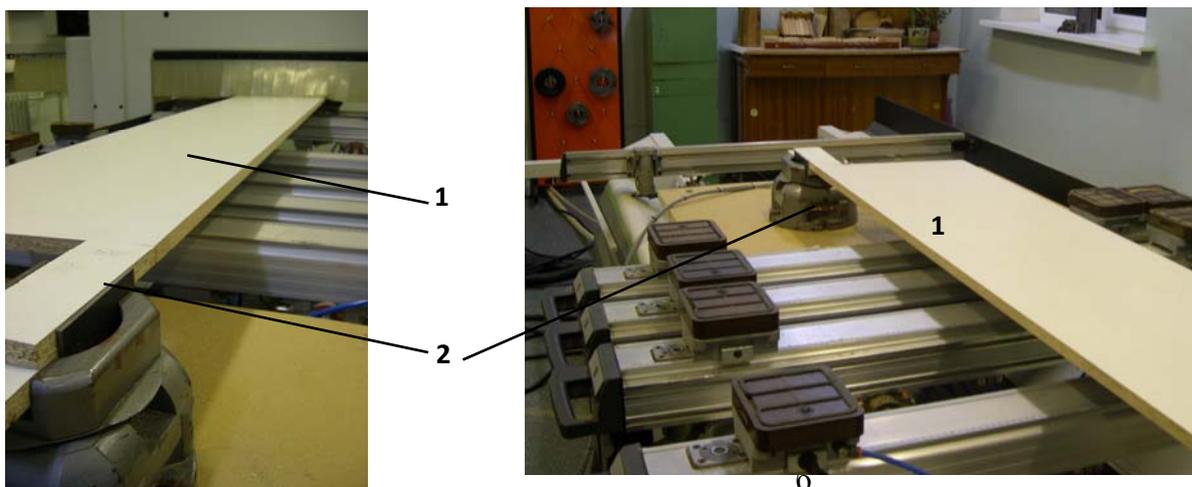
Схема крепления заготовок на рабочих столах станка при проведении экспериментов:
